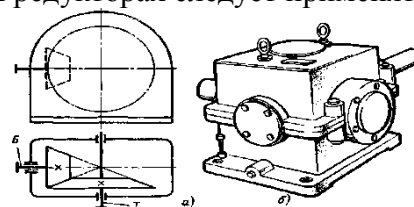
Одноступенчатый редуктор с коническими зубчатыми колесами:
